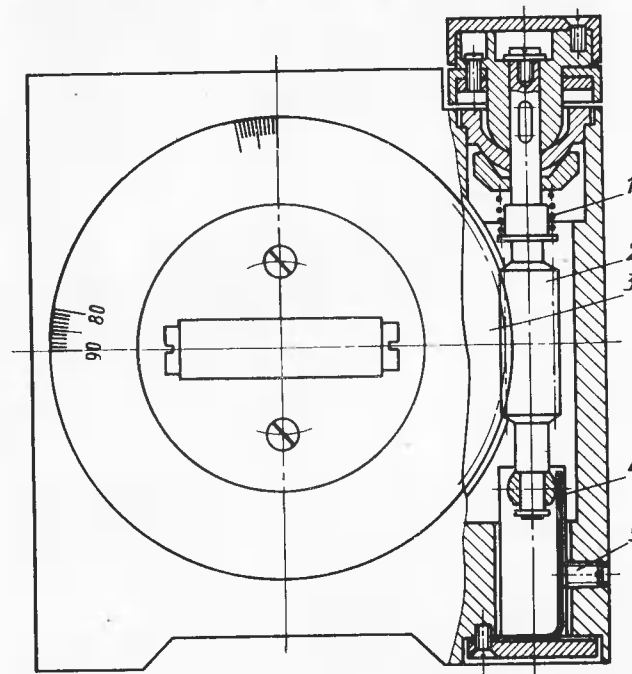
Конструкция узла, обеспечивающего выборку мертвого хода
